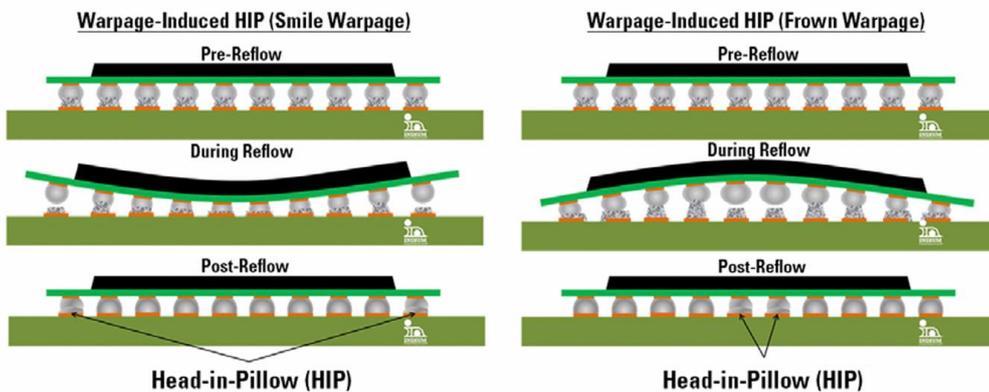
Defecto de soldadura Head-in-pillow
